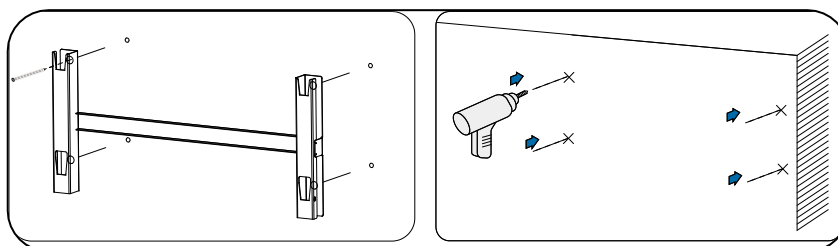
Trapanatura dei fori sulla parete di montaggio
